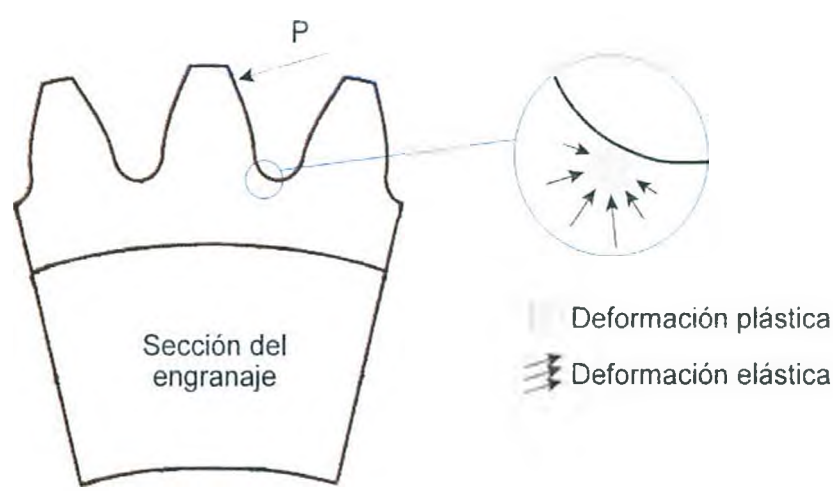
Técnica de preajuste (*presetting*) en engranajes rectos.
